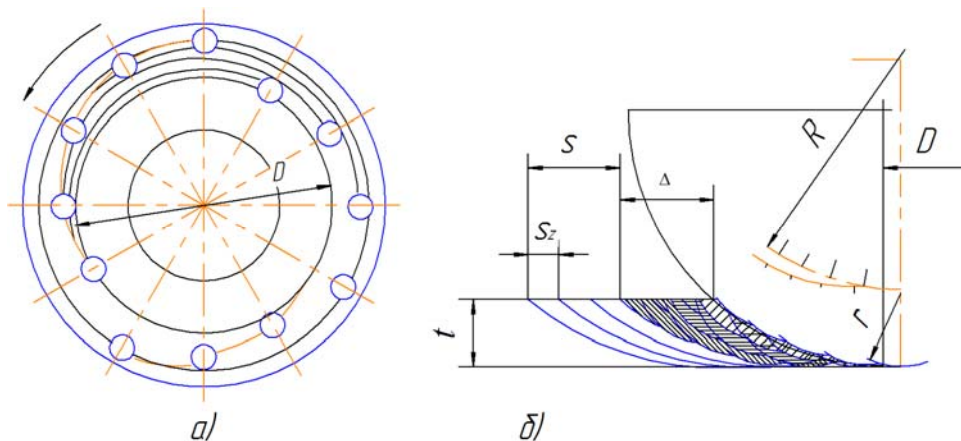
Розташування ножів на корпусі торцевої фрези (а) та схема різання (б)
